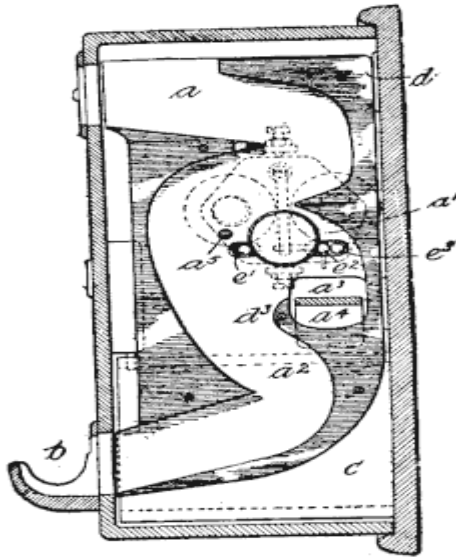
Coupe de la boîte à prépaiement Scribner.
